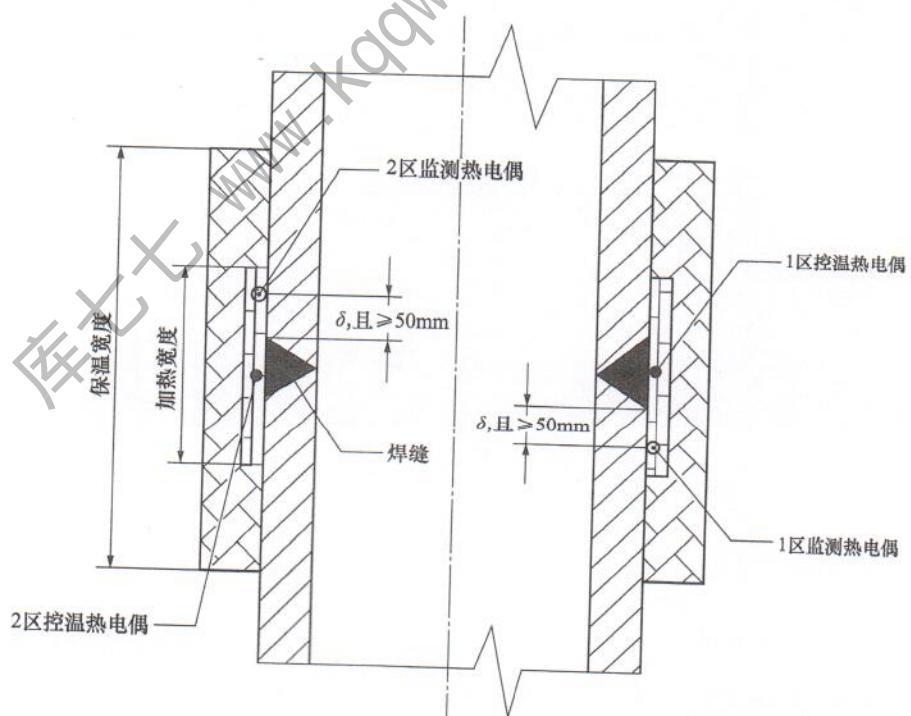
垂直位置管道焊接接头热电偶布置示意
